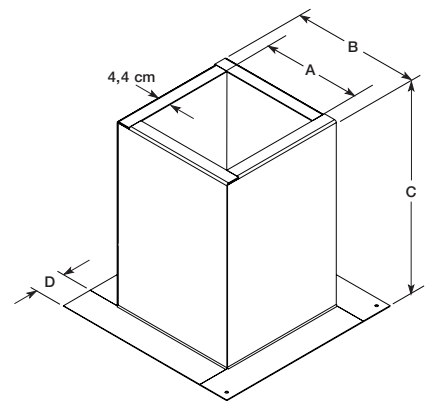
Dimensiones de la Base de Montaje de Techo de Uso Intensivo
